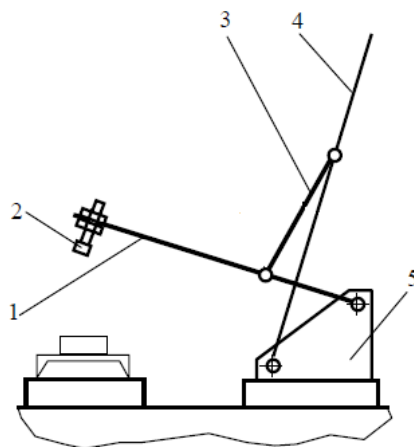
Схема ручного важільно-шарнірного притискача
